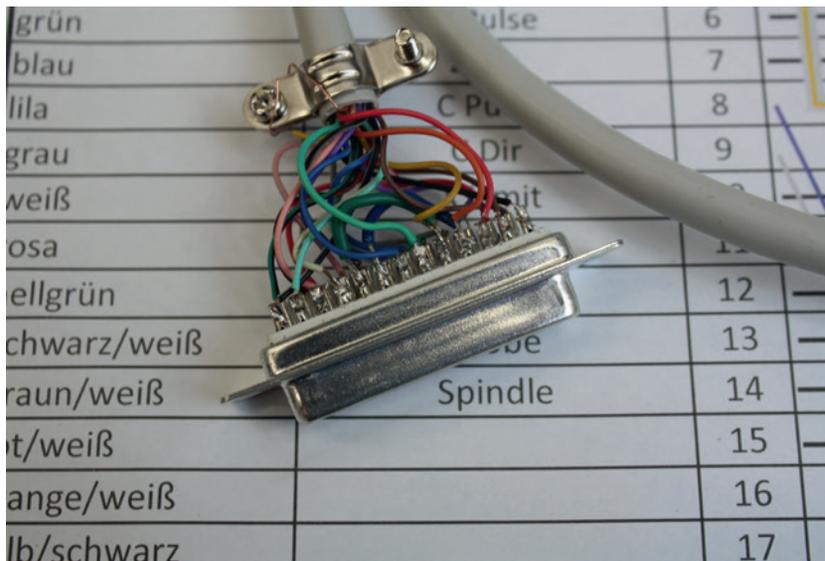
Das Umlöten des Steuerkabels erfordert Fingerspitzengefühl. Die beiden Brücken sind in Blau und Grün zu errahnen.
